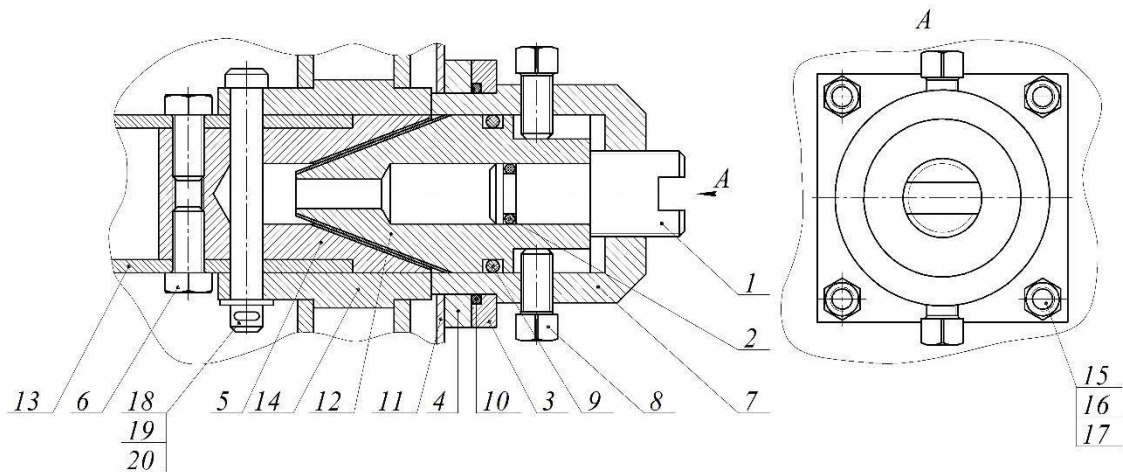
Опора ковзання: 1 – гвинт притискування; 2, 9, 10 – кільце ущільнюоче; 3, 4 – фланець; 5 – вставка; 6 – гвинт; 7 – корпус; 8 – гвинт регулювання; 11 – стінка змішувача; 12 – цапфа; 13 – вал змішувача; 14 – колесо цівкове; 15 – шпилька; 16 – гайка; 17 – шайба; 18 – палець; 19 – шплінт; 20 – штифт
